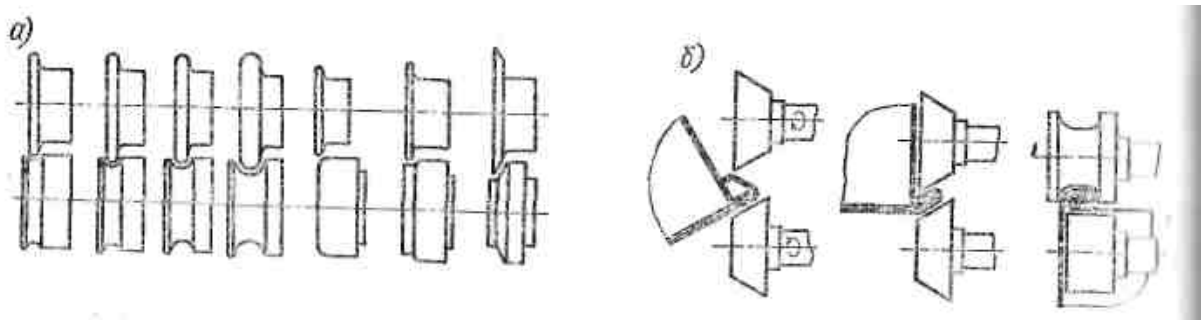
Комплект роликов для накатного станка (а) и закатка соединительных швов
